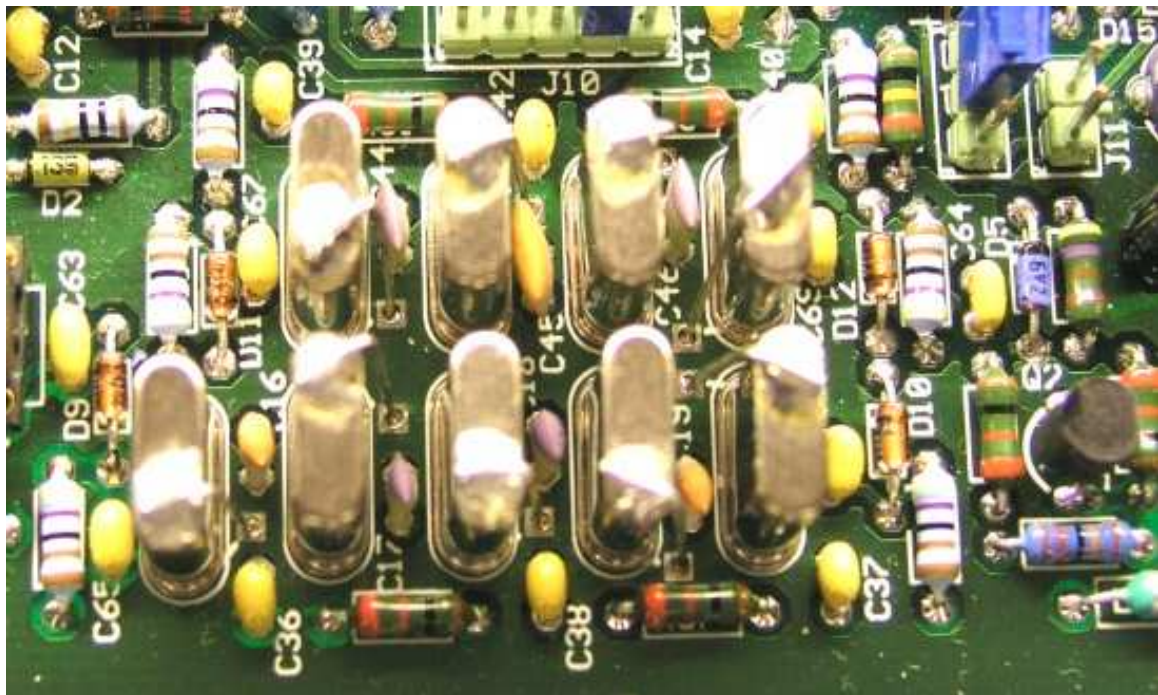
Hauptplatine – Detailansicht SSB-CW-Filter
